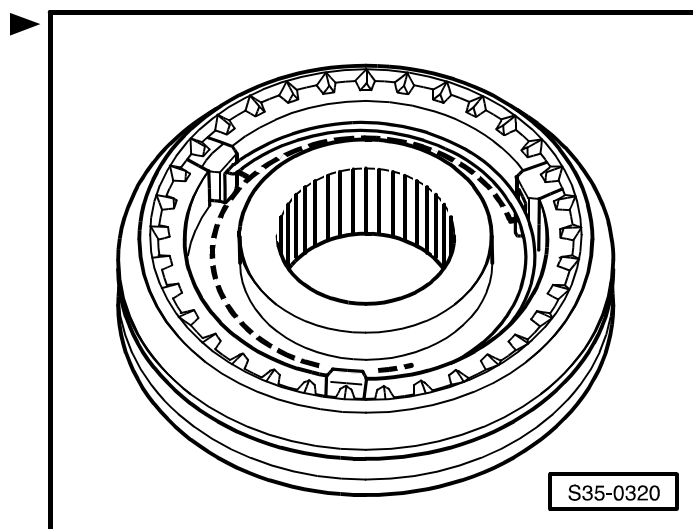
Положение для сборки скользящей муфты и каретки синхронизатора 1-ей и 2-ой передач
